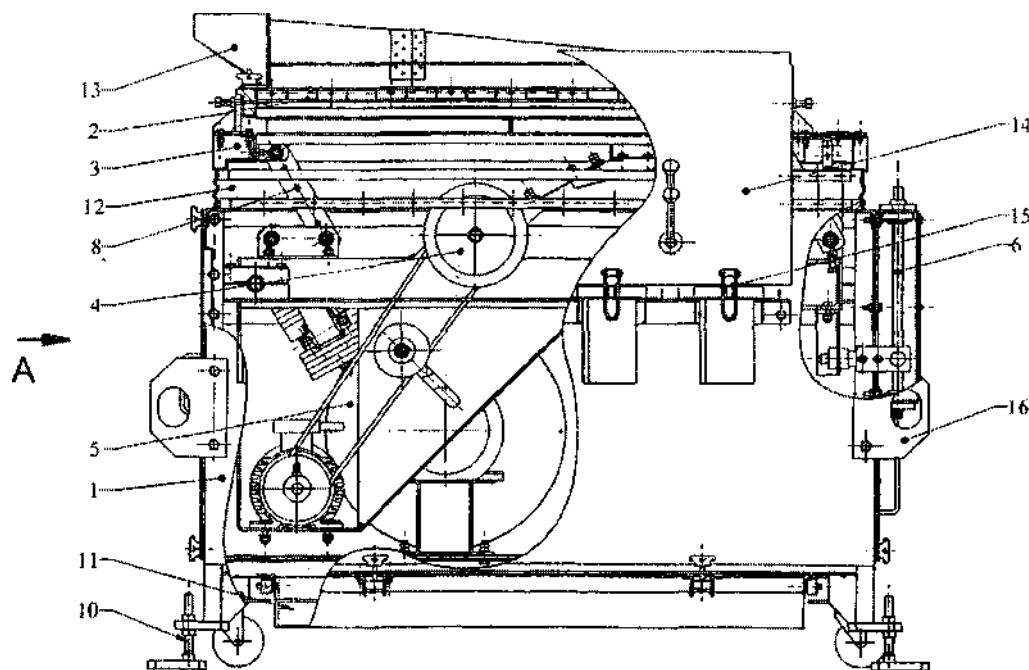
(лист 1 из 2) - Пневматический сортировальный стол ПСС-1.
